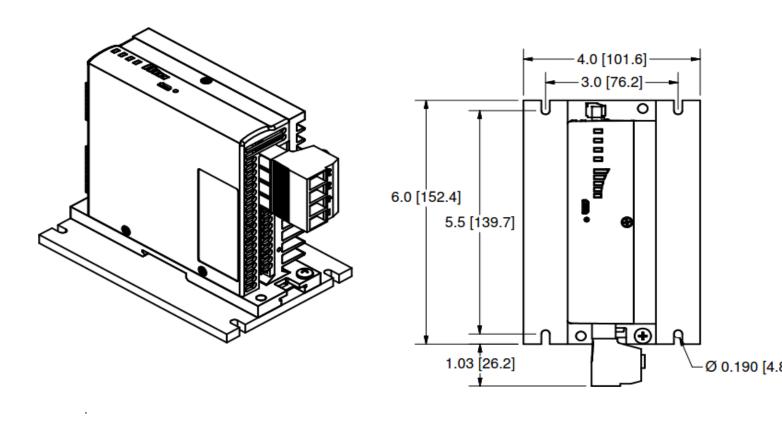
Полноразмерный габаритный чертеж IP-DCR600V15A-R2
